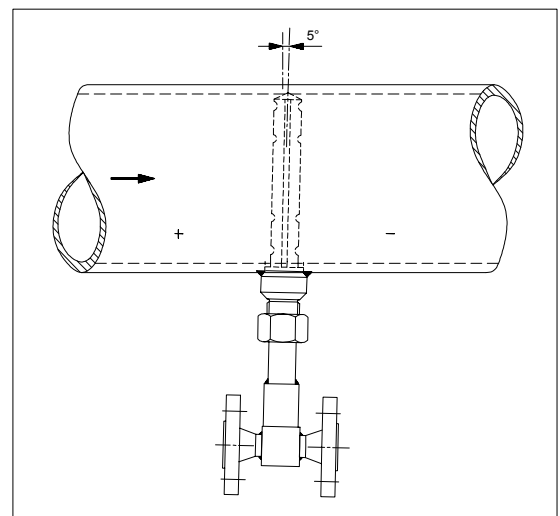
Horizontaler Rohrleitungsverlauf, Draufsicht IBRD-25 ohne Absperrarmaturen
